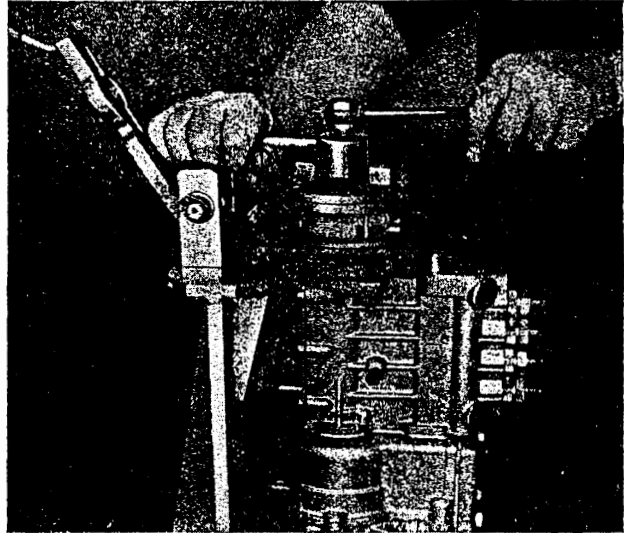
Spritzversteller mit Abzieher (Werkzeug Nr. 324.020-M 118) von der Einspritzpumpe abziehen
